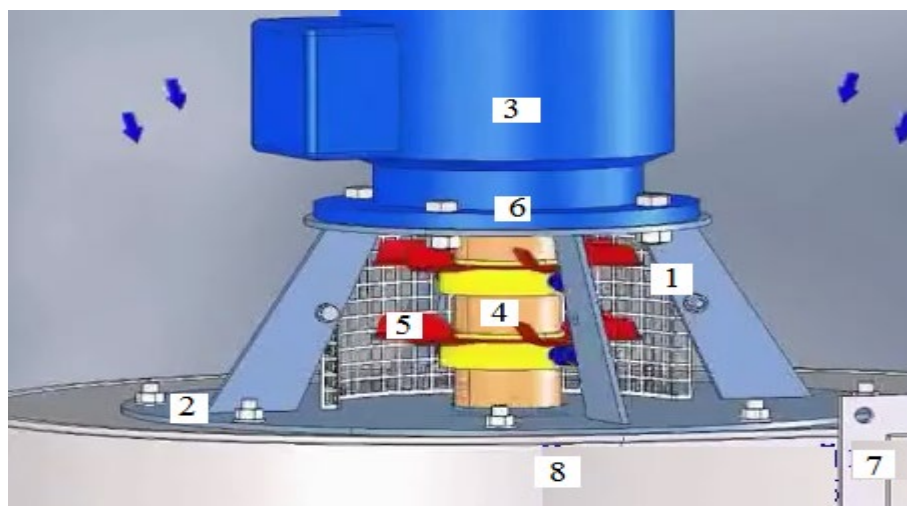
Базова конструкція вакуум-барабана: 1 – корпус; 2 - елементи кріплення; 3 – двигун; 4 – вал; 5 - лопаті нагнітання; 6 – підшипникові опори; 7 – фланець нагнітання; 8 – барабан із лопатями
